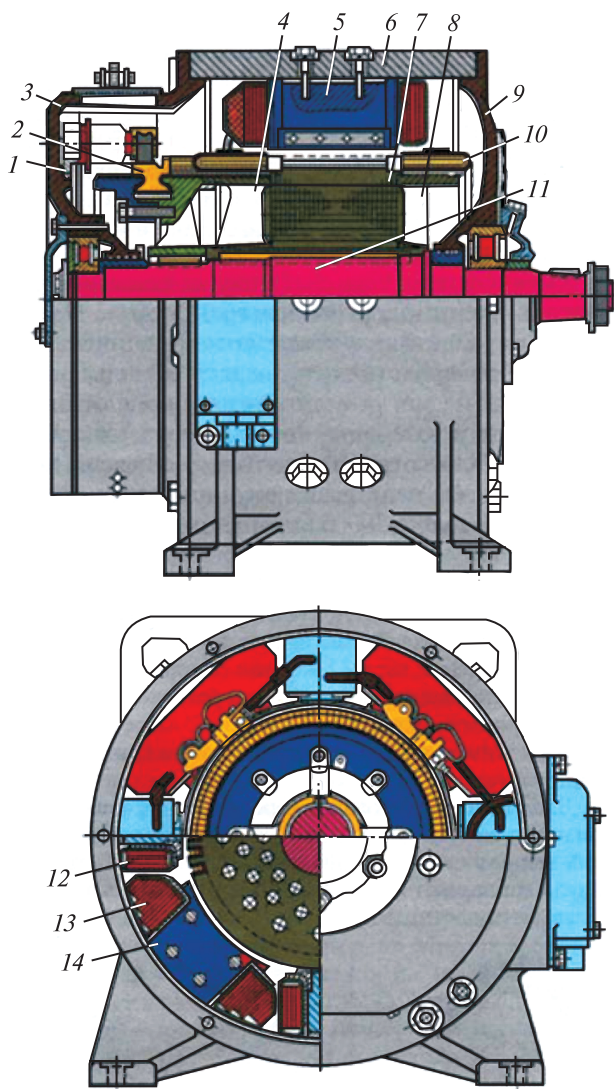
Двигатель ТЛ-122 мотор-компрессора электровоза ВЛ11М:
